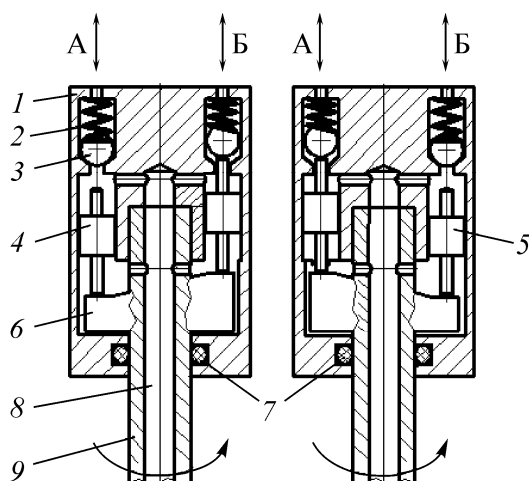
Принципиальная схема двухклапанного гидравлического распределителя для управления скважинным зондом; *A, B* — каналы подачи жидкости в корпус зонда; 1 — корпус распределителя; 2, 3 — пружина и шарик клапана; 4, 5 — толкатели; 6 — эксцентрик; 7 — уплотнение; 8 — канал подачи жидкости от насоса; 9 — напорный трубопровод
